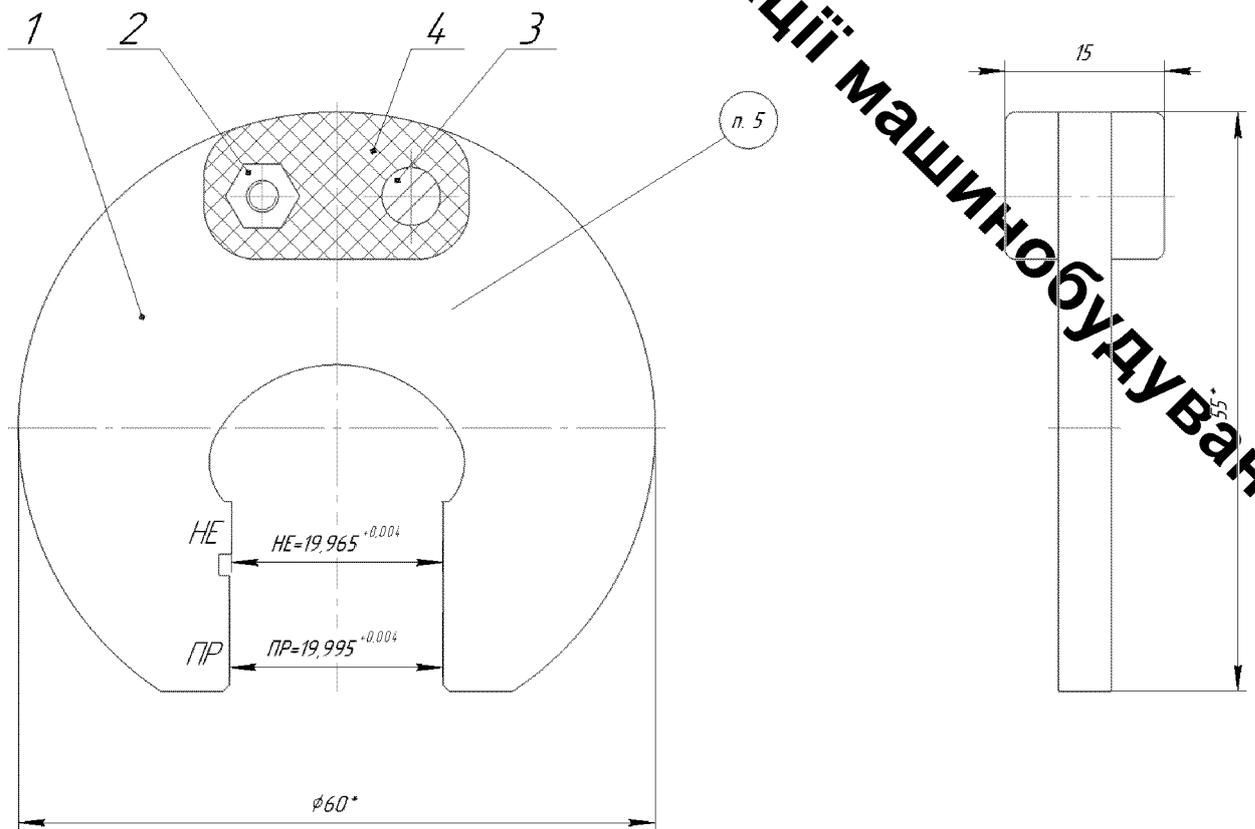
Кресленик калібр-скоби для контролю поверхні $\varnothing 20h8$ мм
